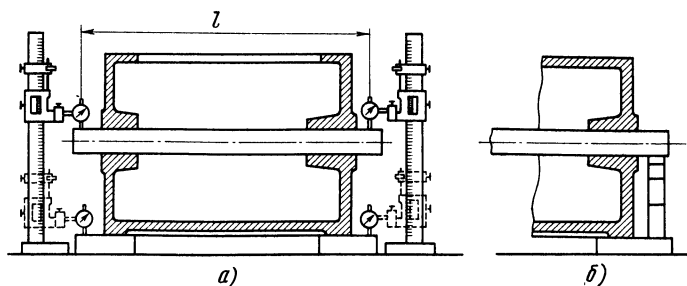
Контроль расстояния от отверстия до базовой поверхности:
